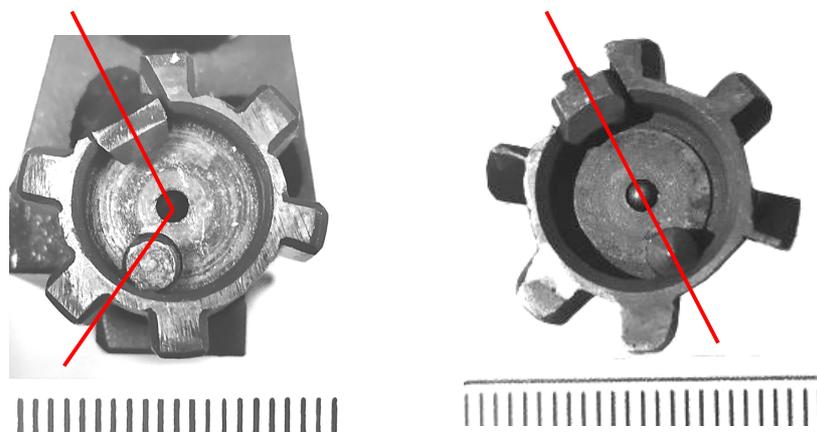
Головная часть (чашки) затвора СОК «МА-Винторез-7,62» (вид слева), ВСС «Винторез» (вид справа)
